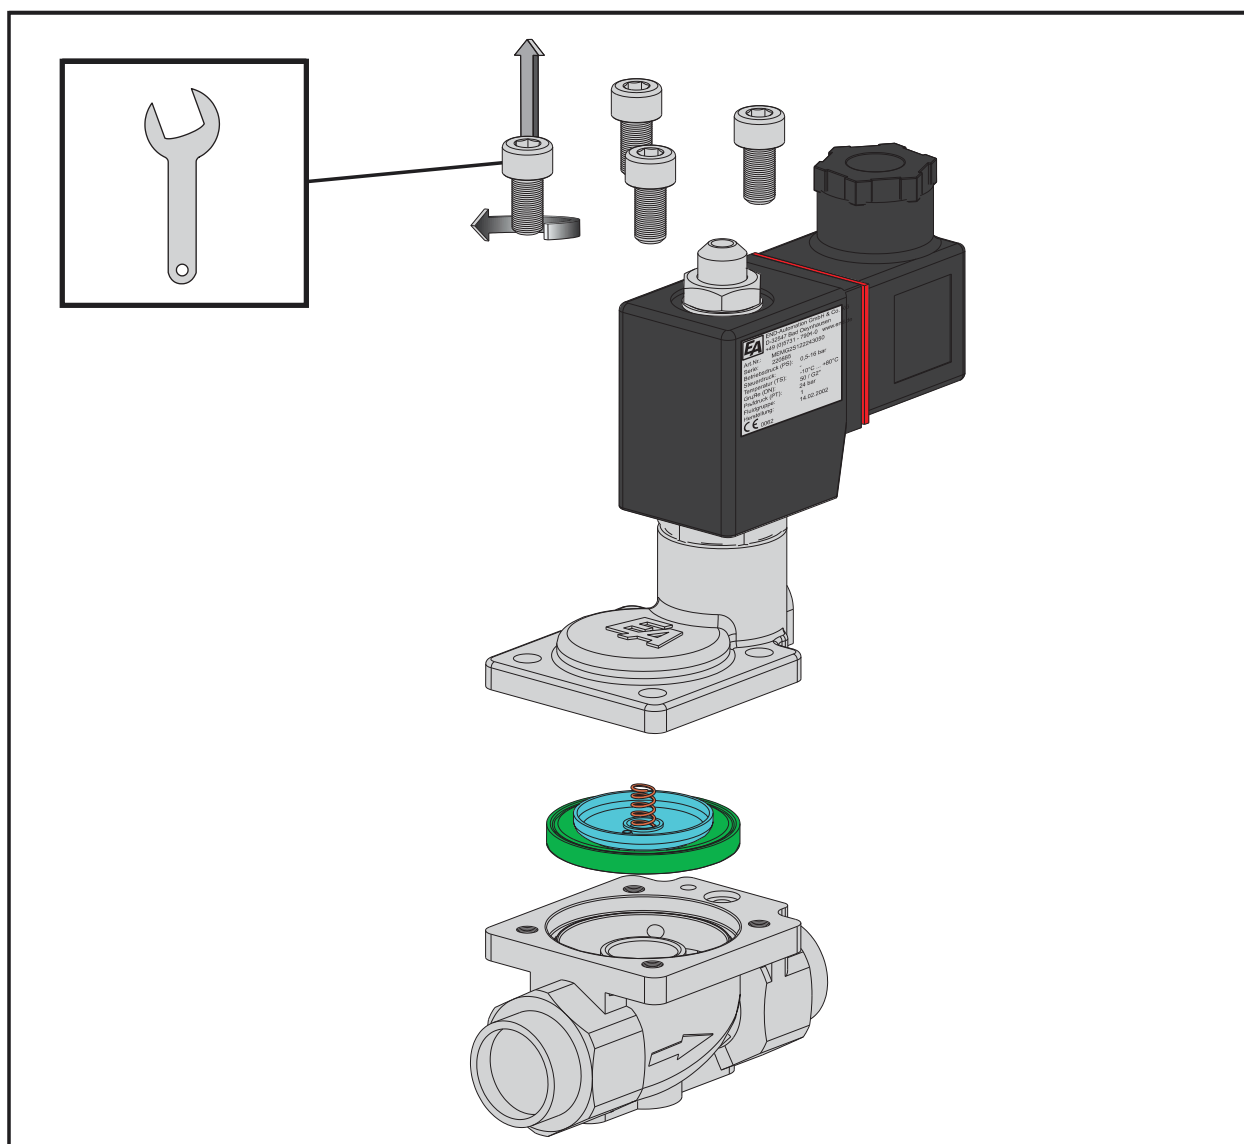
Монтаж/демонтаж – сварное соединение, разборка верхней части клапана
